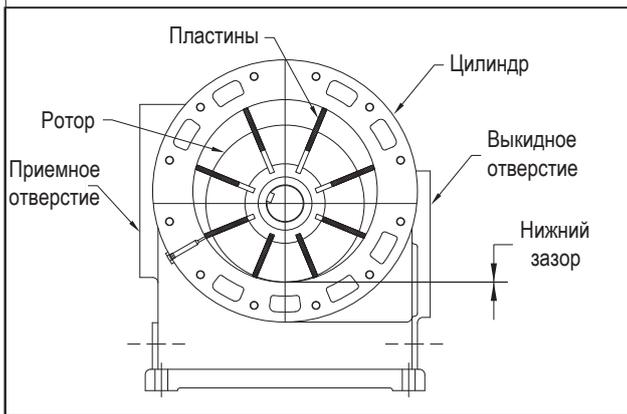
Нижний зазор между ротором и цилиндром (модели низкого давления).
